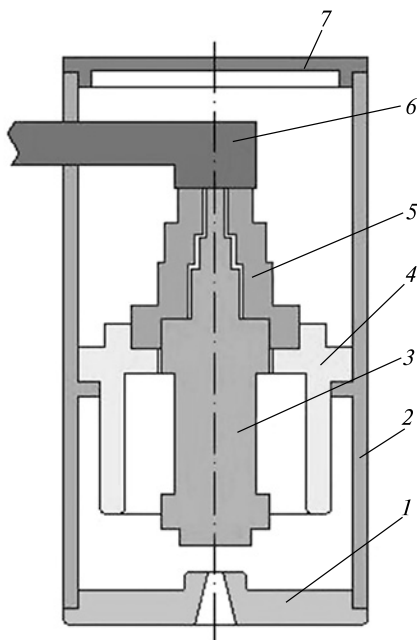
Загальна компоновка нової електронно-променевої зварювальної гармати [11]: 1 — анодний блок, 2 — корпус, 3 — з'ємний катодний вузол, 4 — високовольний ізолятор, 5 — головний ізолятор катодного вузла, 6 — високовольне введення, 7 — кришка
